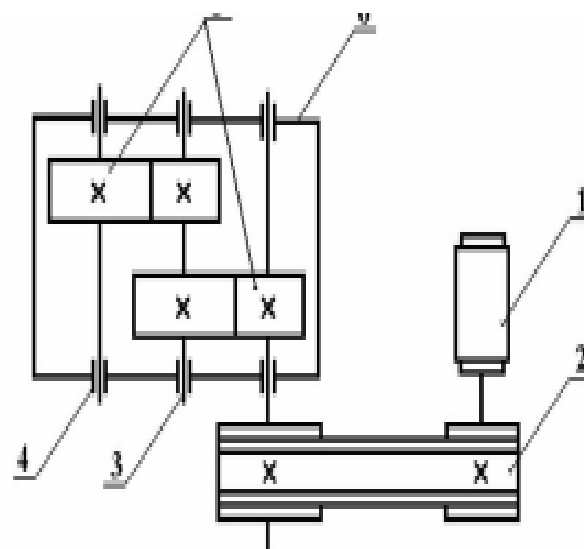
Кинематическая схема привода с цилиндрическим зубчатым редуктором:
